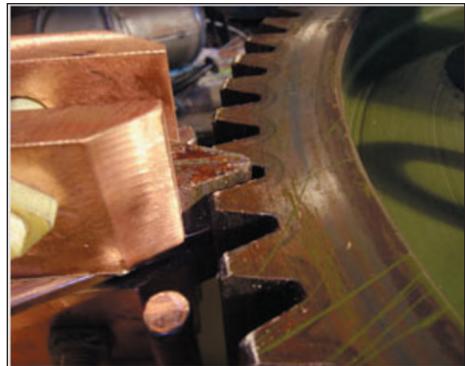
Магнитный концентратор индуктора по впадине зuba для поверхностной закалки ТВЧ
